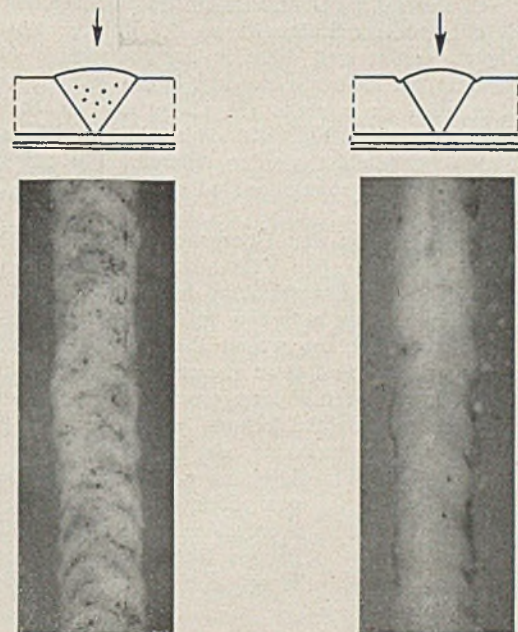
Röntgennegativ einer elektrischen Lichtbogenschweißung mit zahlreichen kleinen Gasporen.
